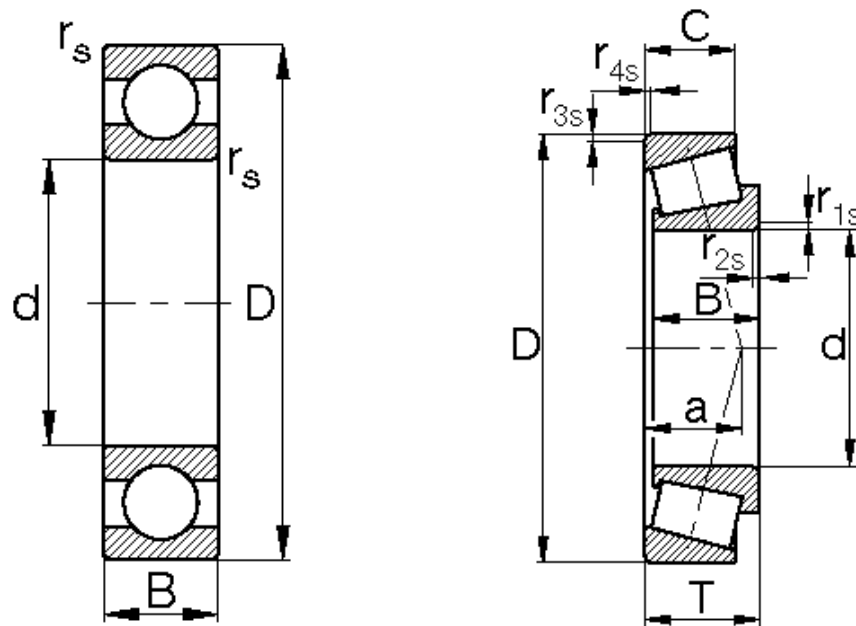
Dimensiones principales de un rodamiento de bolas y de un rodamiento cónico
